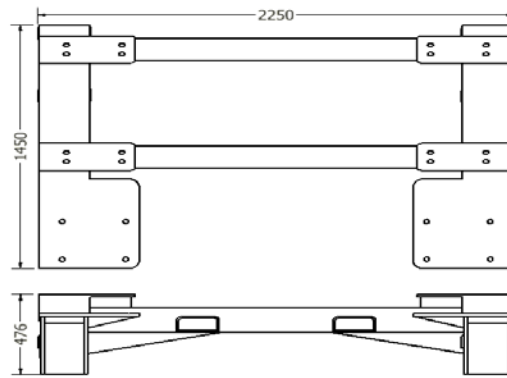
Geometria e dimensões da estrutura de suporte [mm].
